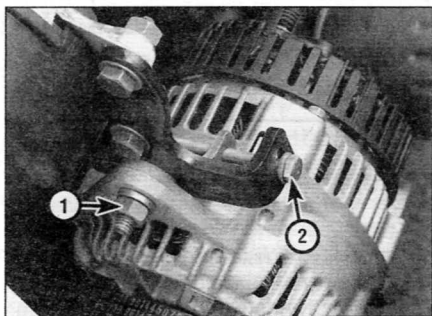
Гайка верхнего крепления генератора (1) и регулировочный болт (2) (двигатели серии XUD)
